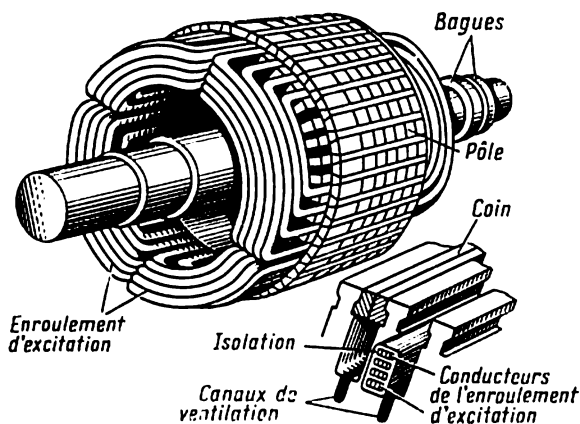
Vue d'ensemble d'un rotor à pôles lisses
